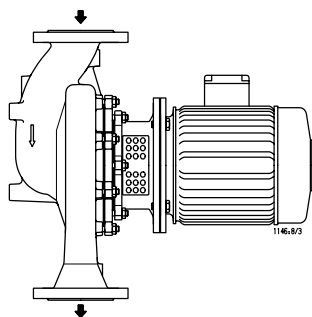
Horizontaler Einbau, Durchflussrichtung von oben nach unten
